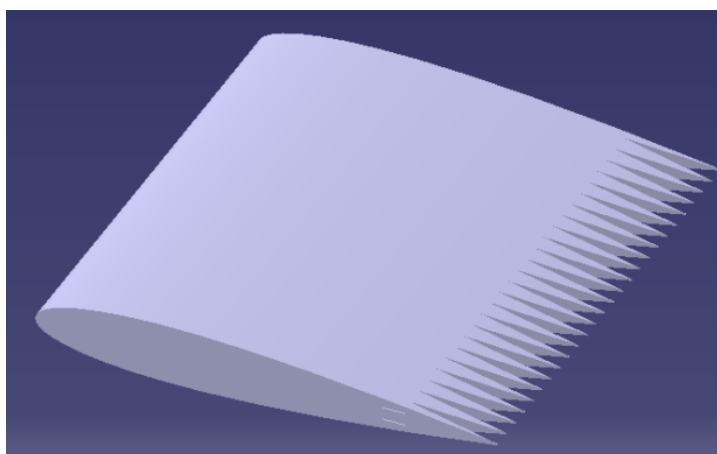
Montagem do perfil no CAD com a inserção do bordo de fuga serrilhado
